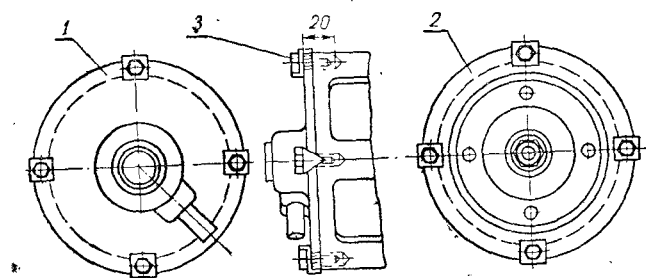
Крепление крышек к корпусу генератора ГБФ-400:
